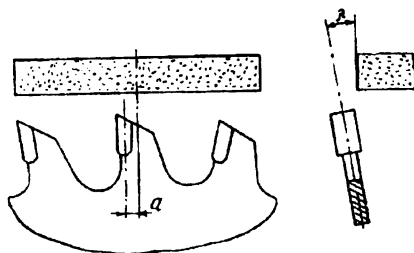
Схема взаимного расположения пилы и шлифовального круга при обработке боковых граней
